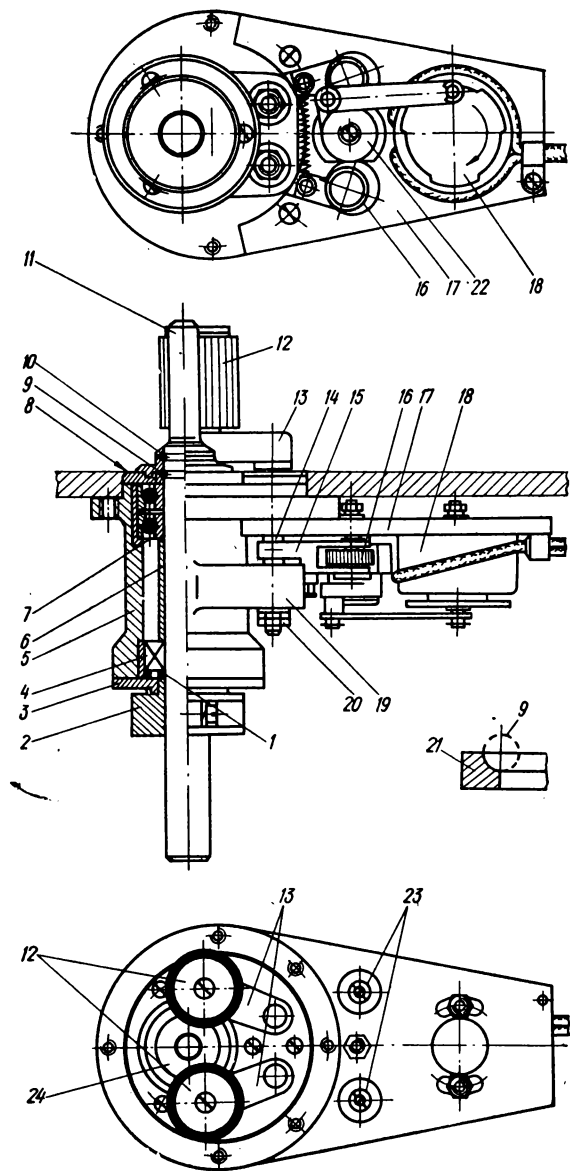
Конструкция прецизионного узла ведущего вала исполнения II.
